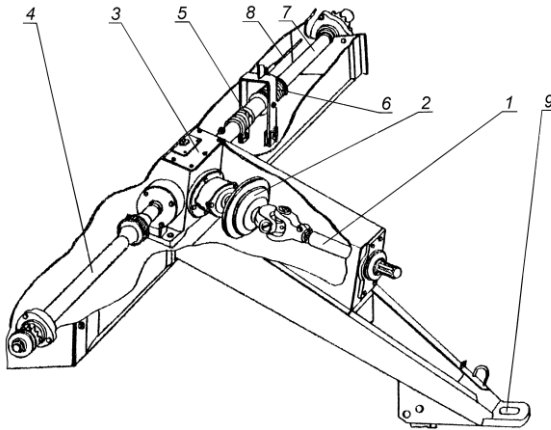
Механизм привода рабочих органов: 1 – вал приема мощности; 2 – предохранительная муфта; 3 – конический редуктор; 4 – вал привода измельчителя и подборщика; 5 – кулачковая муфта; 6 – пружина; 7 – вал привода прессующего механизма и вальцов; 8 – тяга; 9 – сница.
